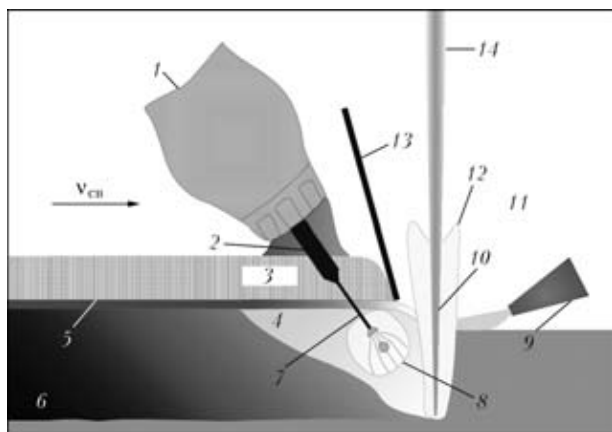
Схема гибридной лазерно-дуговой сварки под флюсом: 1 — бункер для флюса; 2 — контактная трубка; 3 — флюс; 4 — жидкая ванна; 5 — твердый шлак; 6 — металл шва; 7 — проволоочный электрод для дуговой сварки под флюсом; 8 — полость шва с дугой; 9 — струя гелия; 10 — парогазовый канал; 11 — жидкий шлак; 12 — плазма с парами металла; 13 — разделительная пластина; 14 — лазерный луч
